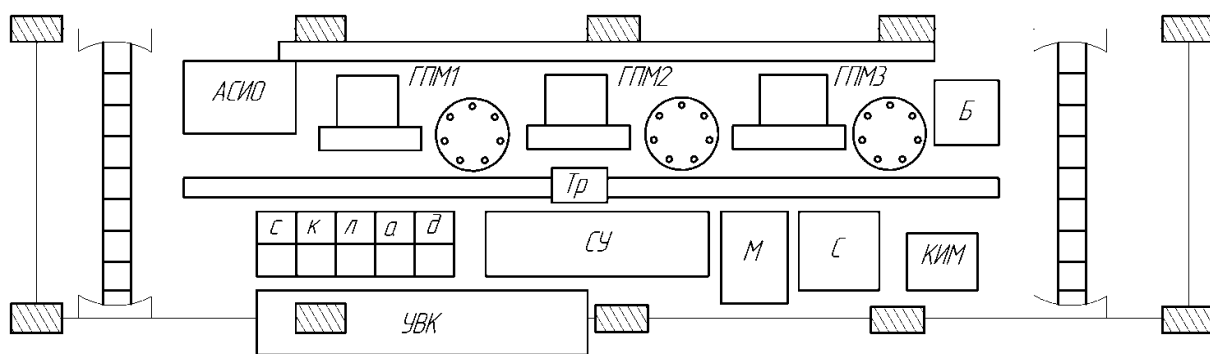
План ГАД зі свердлильно-фрезерно-розточувальними ОЦ
